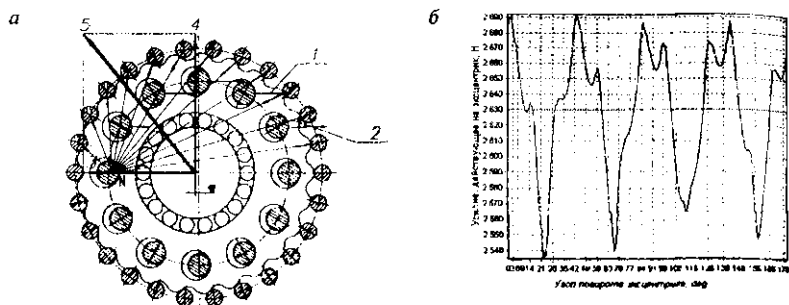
Нагружение эксцентрика: *a* – схема усилий, действующих в планетарно-цевочном редукторе; *b* – циклы нагружения эксцентрикового узла: 1 – усилие со стороны одного из пальцев механизма параллельных кривошипов; 2 – со стороны цевки цевочного колеса; 3 – горизонтальная, 4 – вертикальная, 5 – суммарная составляющая усилия, действующего со стороны эксцентрика
